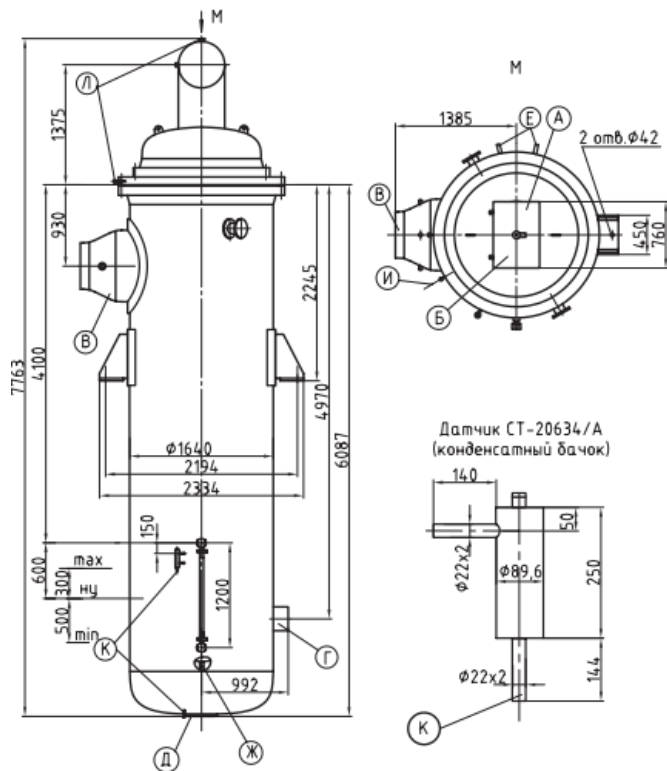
Общий вид подогревателя ПСВ-500-14-23 [12]
